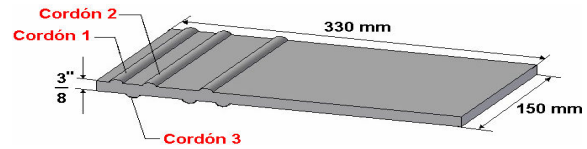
Material base y disposición de los cordones de soldadura para cada velocidad de alimentación del electrodo
